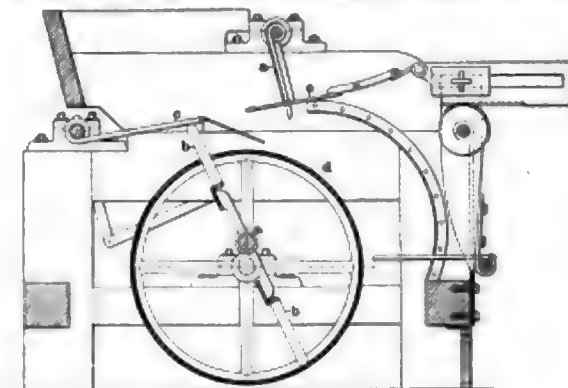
Einlegervorrichtung für Dreschmaschinen.
